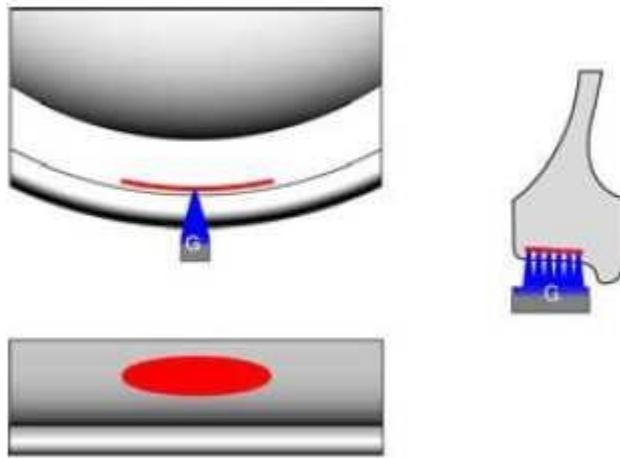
INSPECCIÓN EN BUSCA DE DEFECTOS "SHATTERING"
